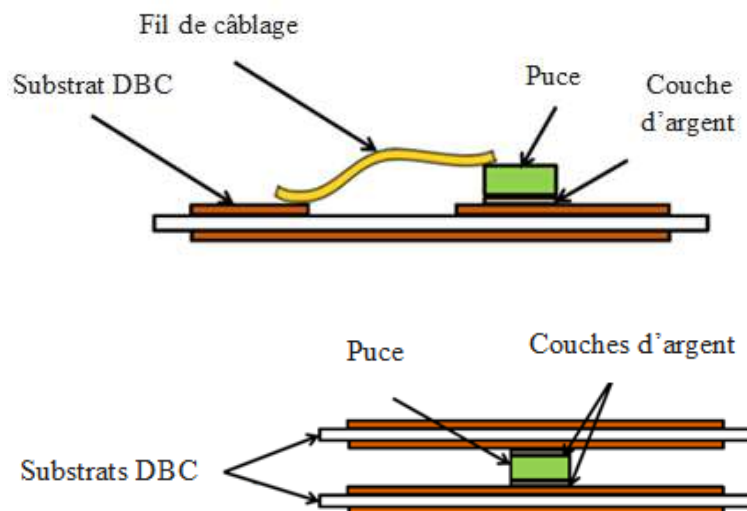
Représentation schématique d'un assemblage classique et d'un assemblage double face
